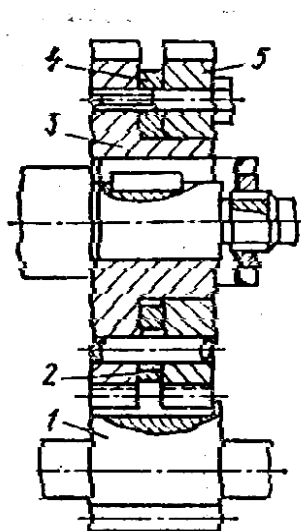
Схема усунення зазору в редукторі поперечної подачі верстата 6Р13Ф3-37
